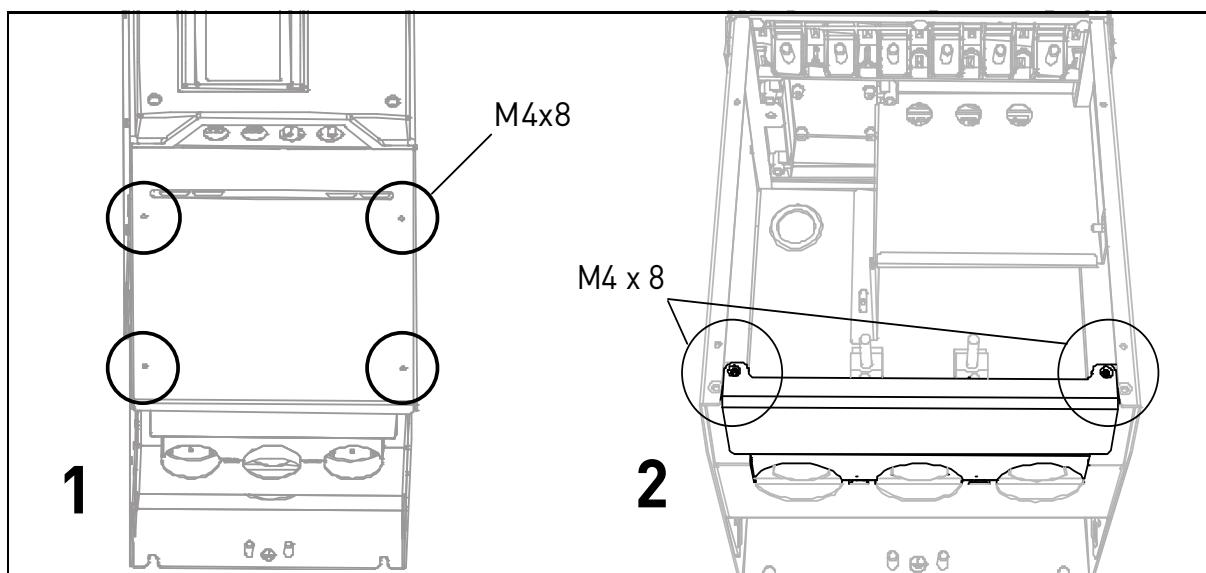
Removendo a tampa do cabo e a placa de fixação do cabo (MR8).
